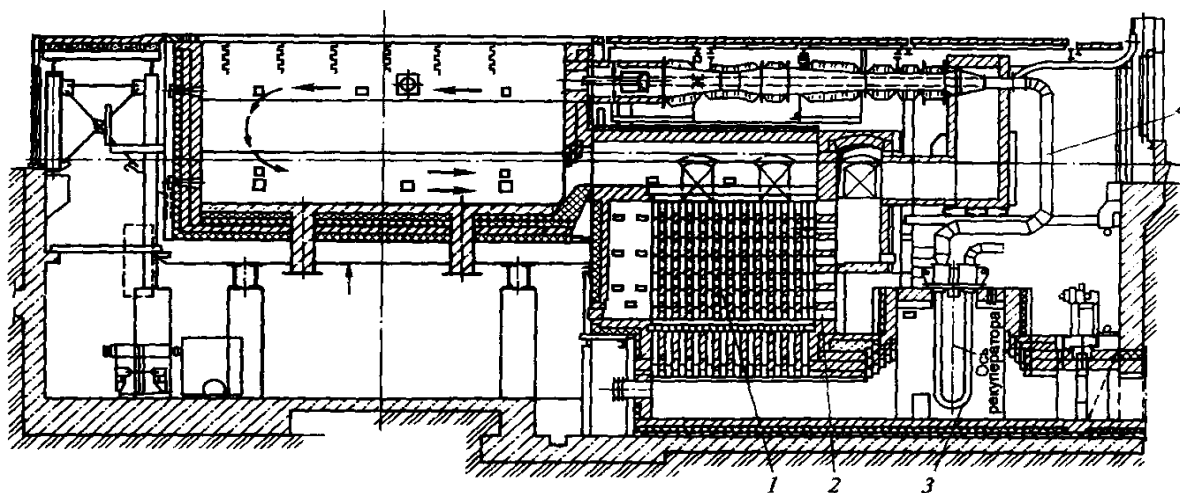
Рекуперативный нагревательный колодец с одной верхней горелкой: 1 – керамический рекуператор; 2 – каналы для входа холодного воздуха; 3 – металлический рекуператор для нагрева сжатого воздуха; 4 – подвод сжатого воздуха в инжектор
